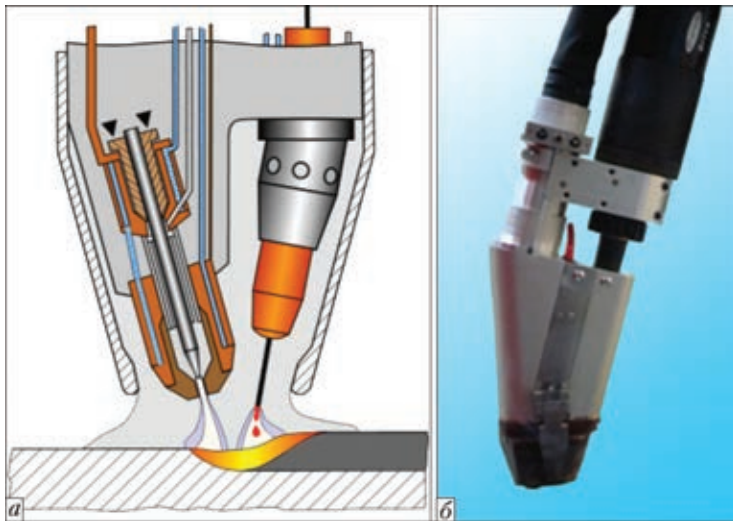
Схема процесса (а) и сварочная горелка для процесса Super-MIG (б)
